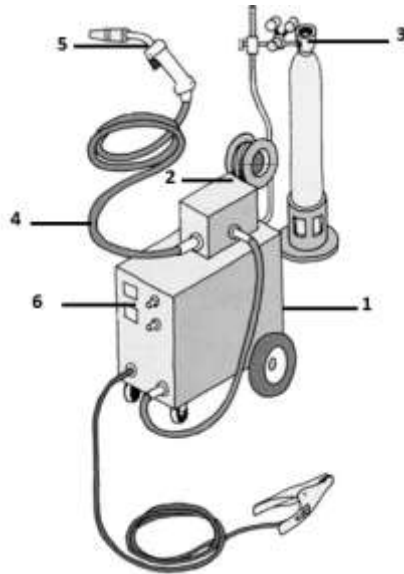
Componentes suelda MIG (HERRAMIENTAS, 2012)
